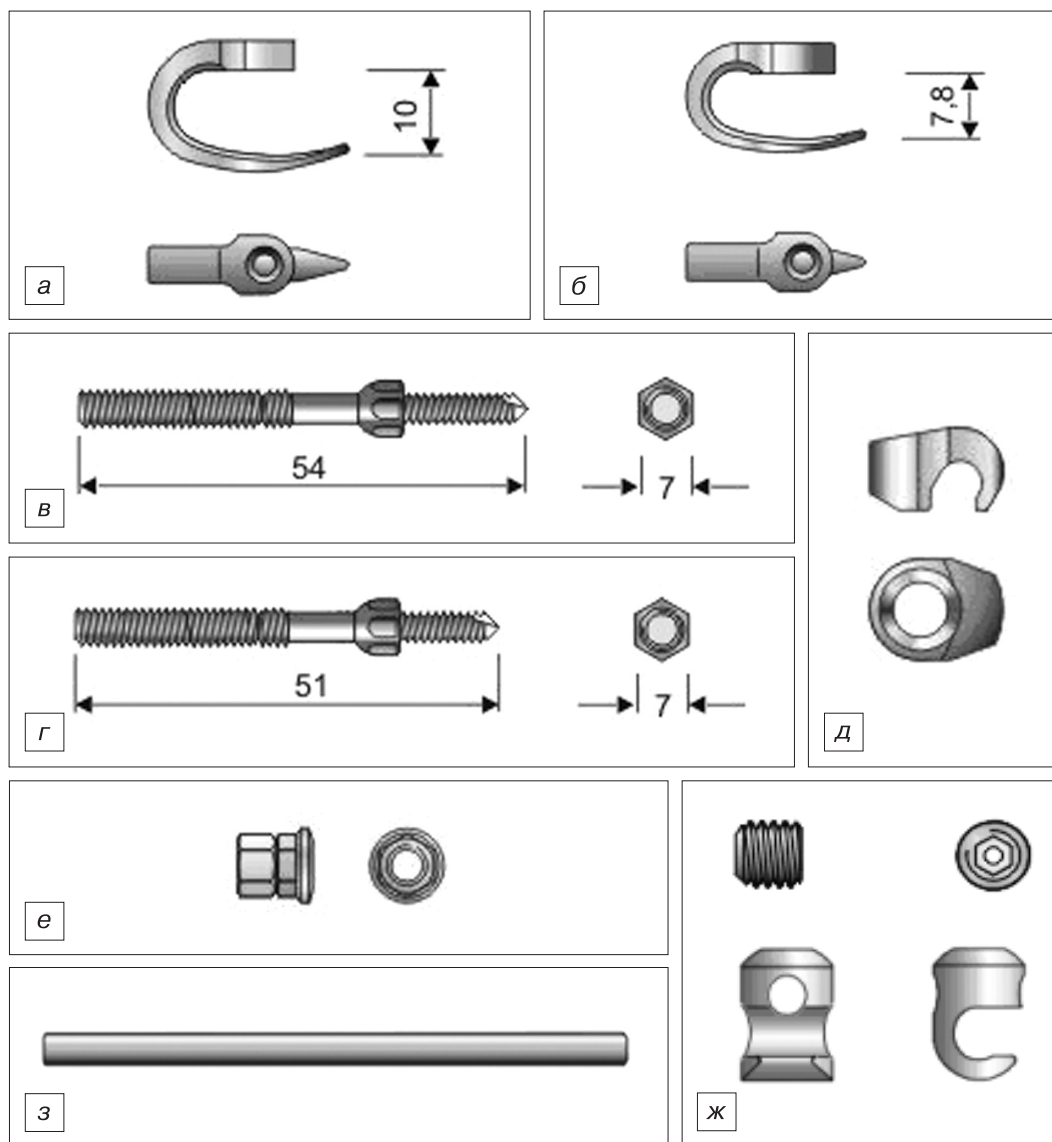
Элементы блока крепления конструкции LSZ-3.
